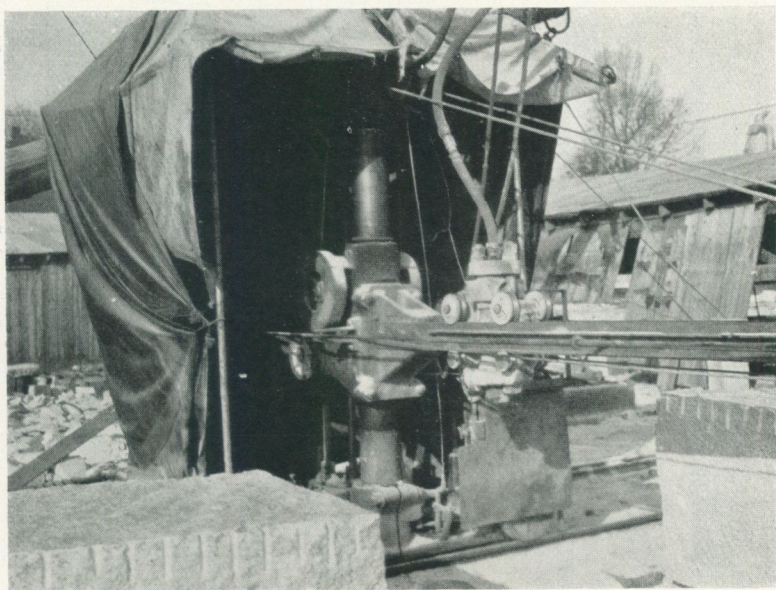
Stor surfacermaskin med motordriven förflyttning. Mount Airy. Sid. 34.
